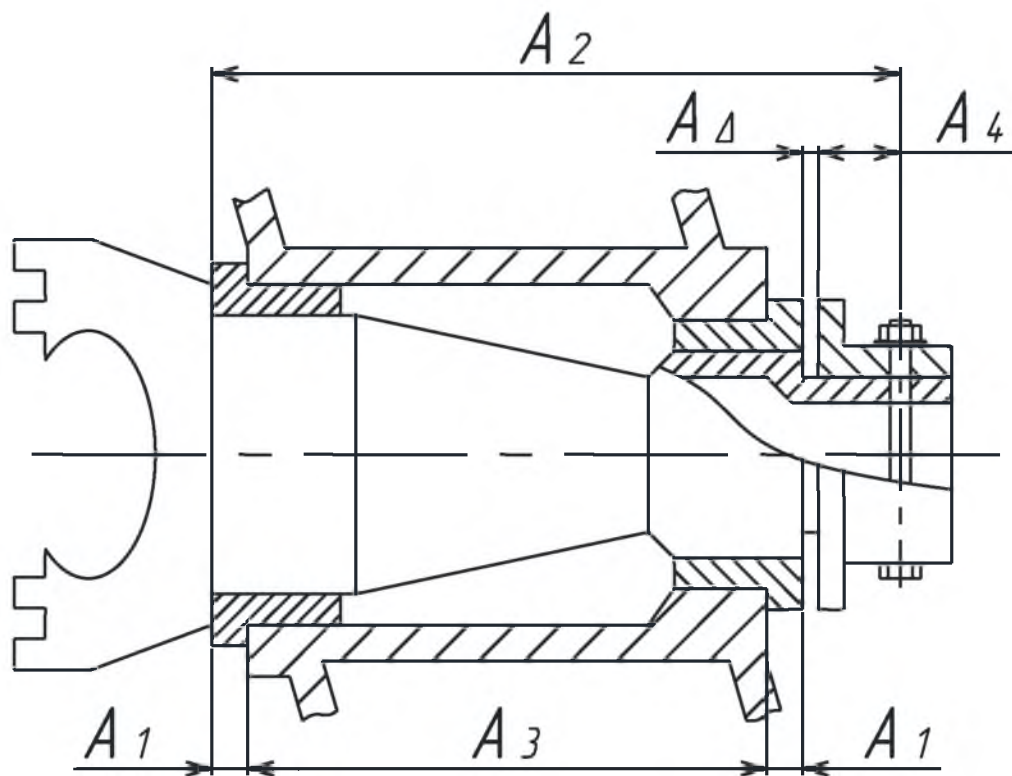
Эскиз крепления винтового механизма трехщелевого закрывка
